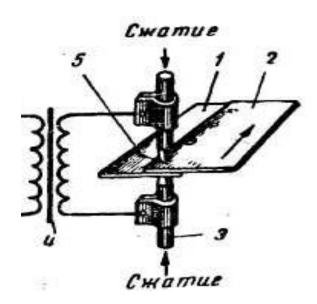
Схема процесса контактной точечной сварки
